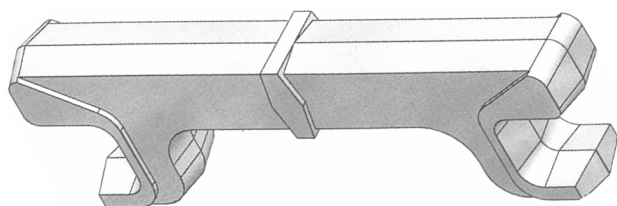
Колосник с дополнительными выступами на боковой поверхности [9]
